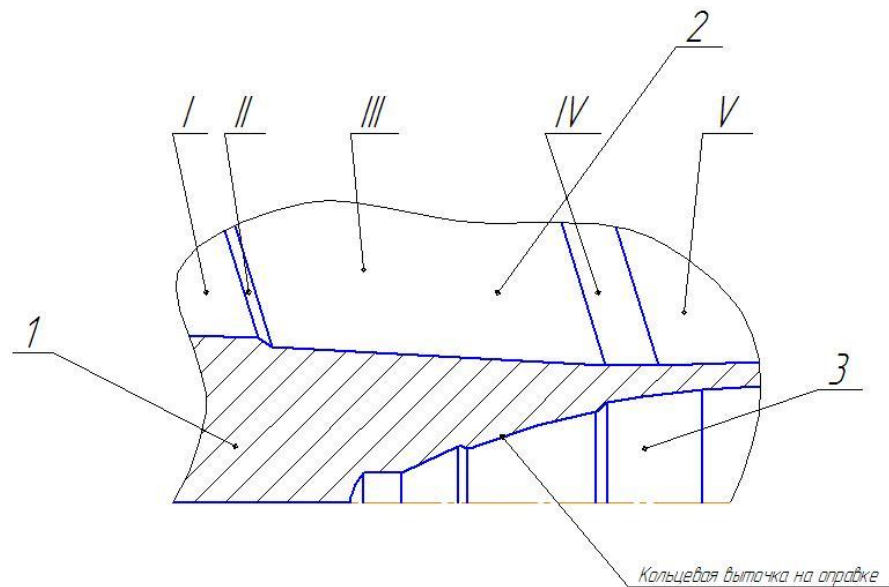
Схема очага деформации для прошивки заготовки повышенного диаметра и расположение функциональных участков на валке прошивного стана: 1 – прошиваемая заготовка; 2 – валок, включающий участки: I – «захватной»; II – гребень интенсивной деформации; III – «обжимной выступ»; IV – пережим; V – раскатной; 3 – оправка
